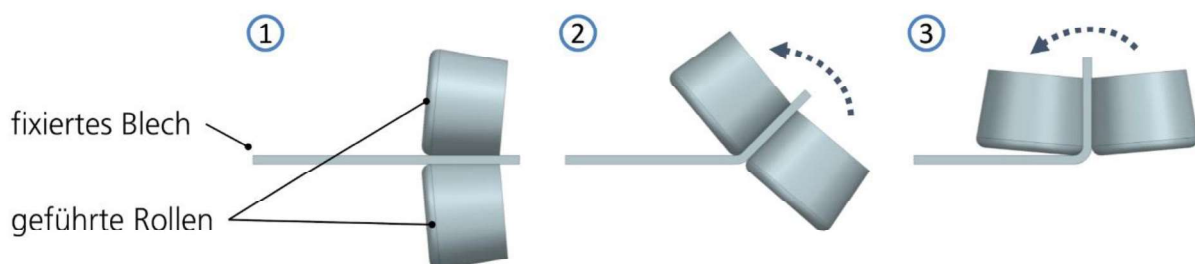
Verfahrensprinzip des roboterbasierten Rollformens [9]
